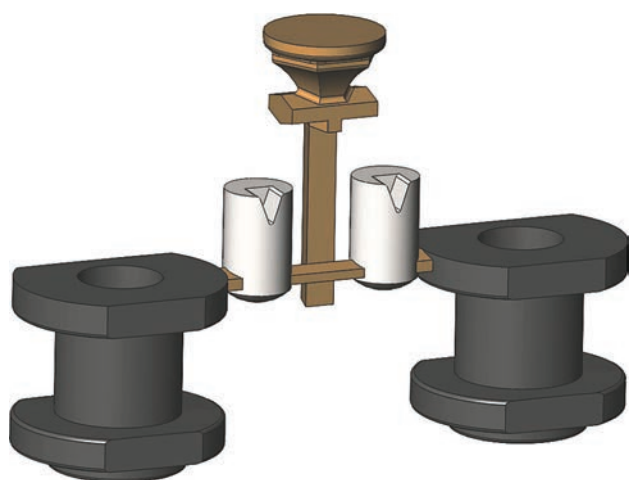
Отливки «Корпус» с литниково-питающей системой
